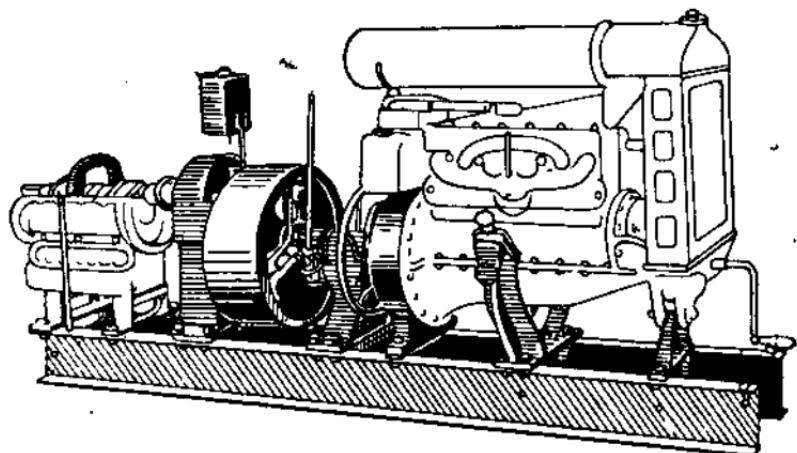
Станок «Кеннеди-Отто» для прижигания и приработки подшипников.
